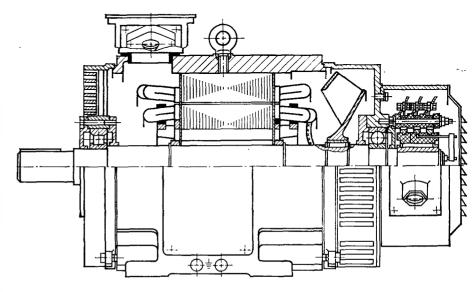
Асинхронный двигатель с фазным ротором 4АНК200, степень защиты IP23
